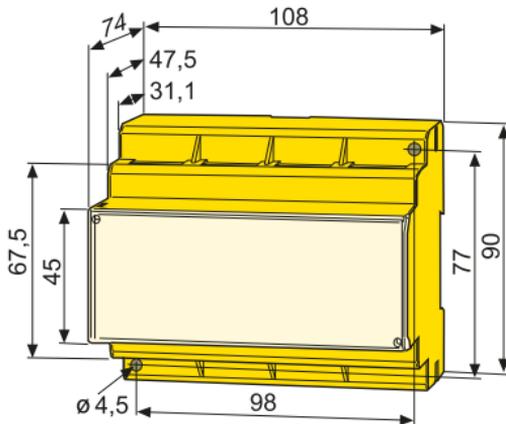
Maßbild, Skizze für Schraubbefestigung
